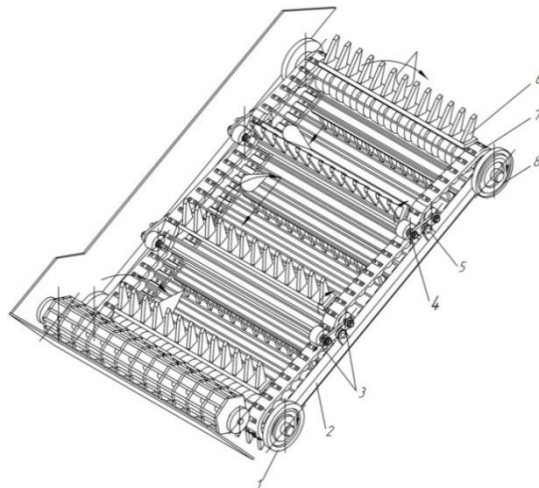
Конструктивна схема скребкового транспортера-доочисника коренеплодів
